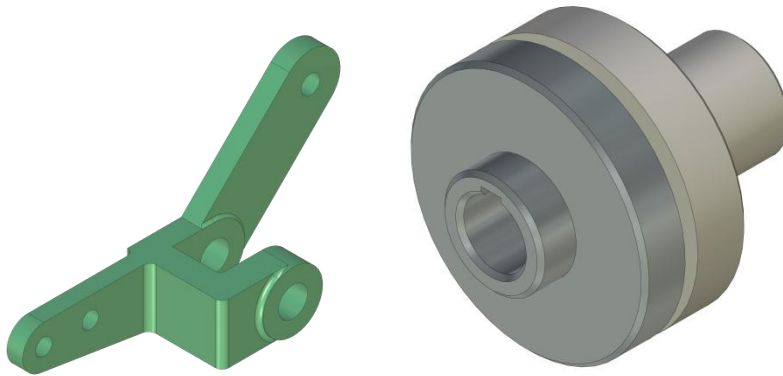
Трёхмерная модель детали и модель сборки муфты.
